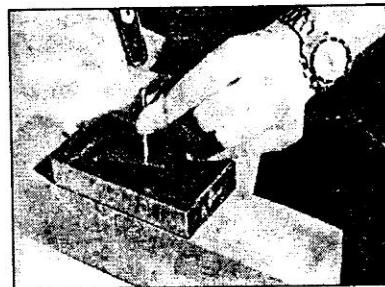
Имитация заклепки штамповкой с тыльной стороны пластины
